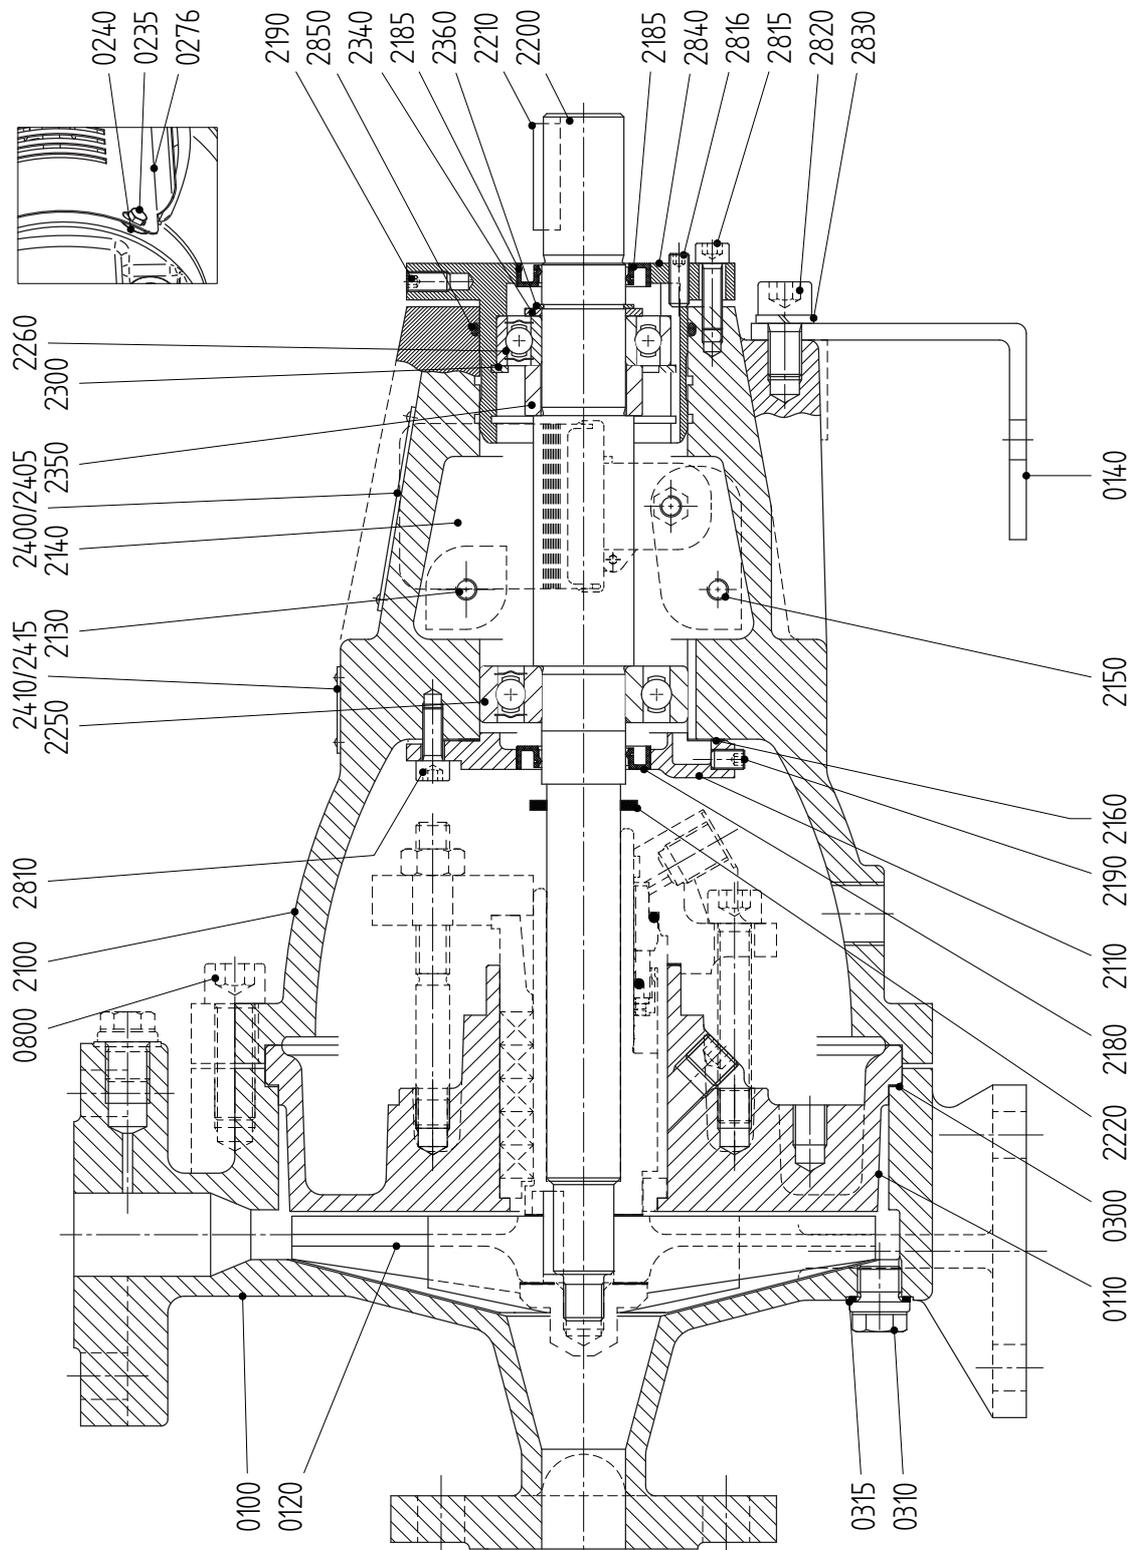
Schnittzeichnung L5 / L6 - 25-....
